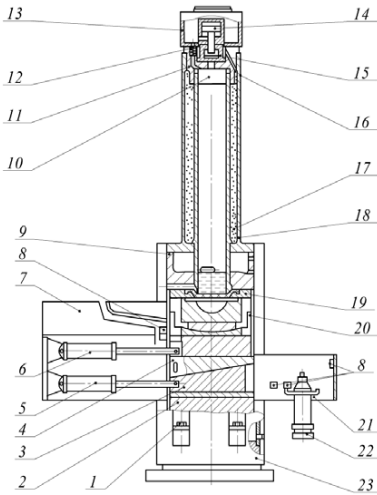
Конструкція машини Т-1324М: 1 – анкерний болт; 2 – станина; 3 – клин; 4 – контрclin; 5, 6 – гідроциліндри; 7 – глушник; 8 – кінцеві вимикачі; 9 – робоча камера; 10 – бойок; 11, 19 – фланці; 12, 15 – клапани; 13 – кожух; 14 – пусковий механізм; 16 – цанга; 17 – ствол; 18 – акумулятор; 19 – манжета; 20 – контейнер з сферичною основою; 21 – напрямні; 22 – виштовхувач; 23 – шочи
